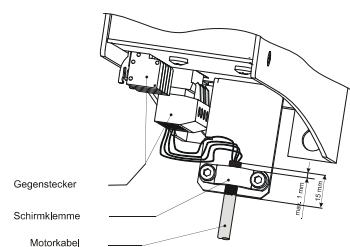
Motorgegenstecker für die SM-Serie (Gewinde M40)
